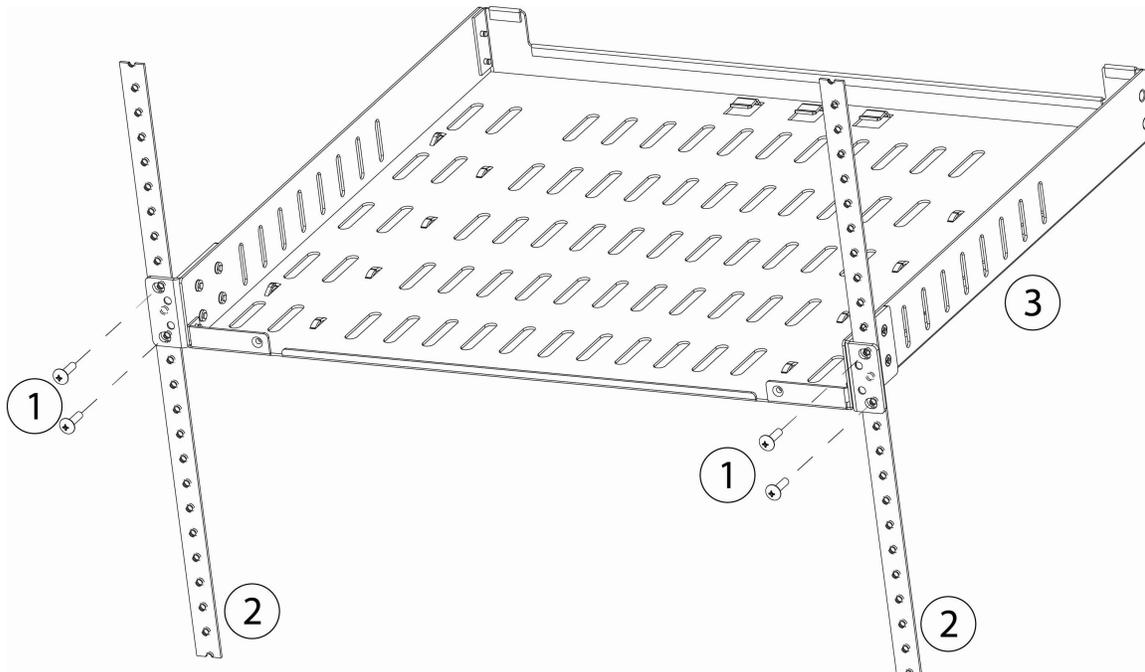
Installer les supports de montage sur la tablette de montage en rack
